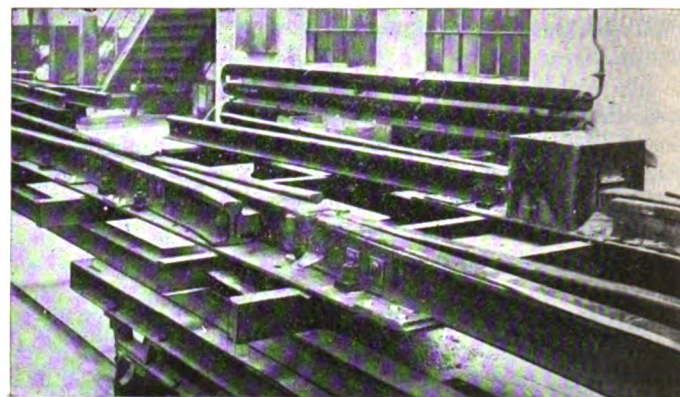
Herzstück, nach dem Zwischengußverfahren mit Lichtbogenauftrag verschweißt, im Rohzustand.
